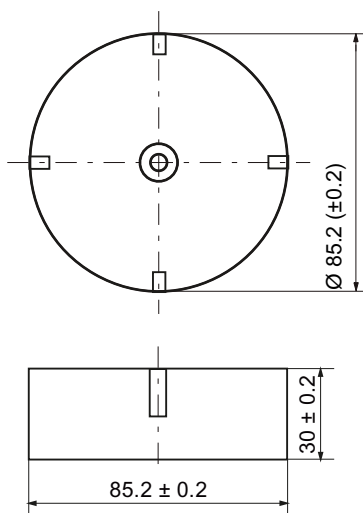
垫片 6GT2690-0AA00 的尺寸图
